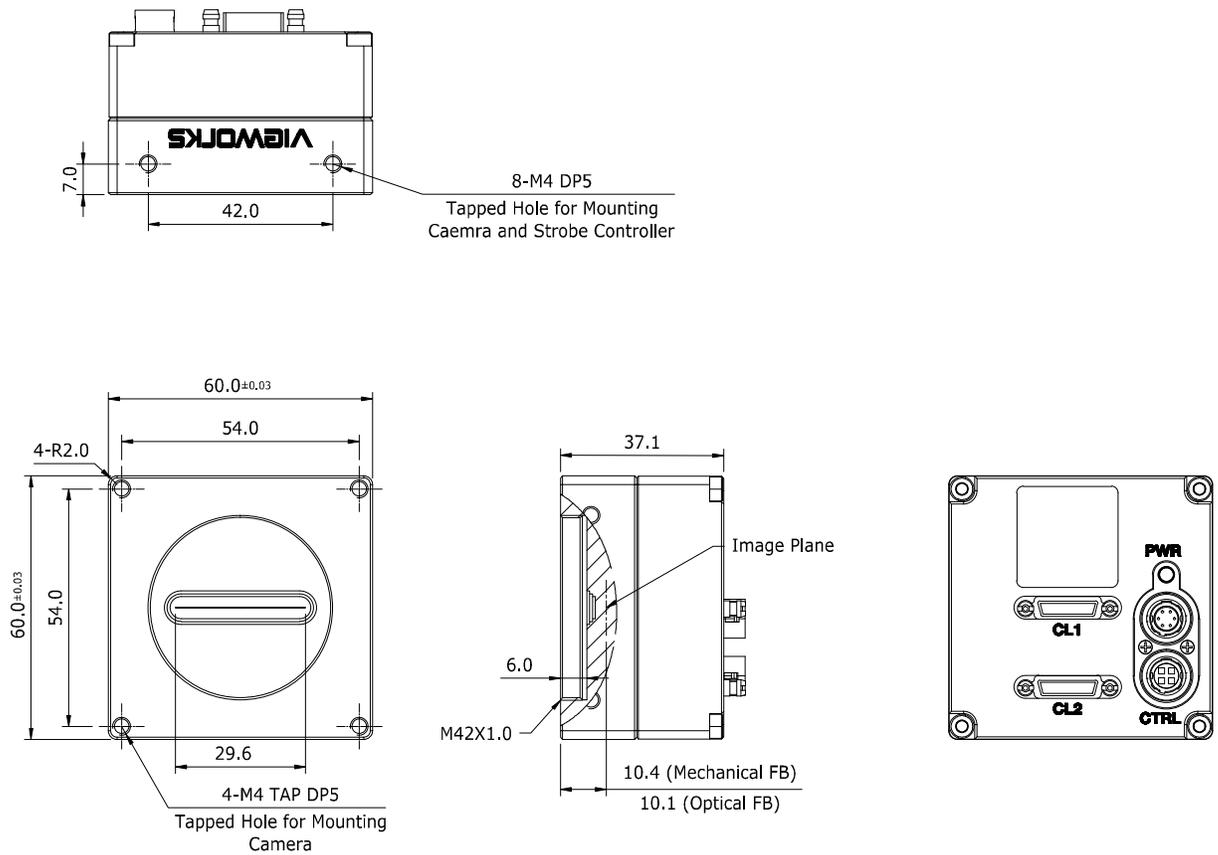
VL-2K/4K 시리즈 Mechanical Dimension
